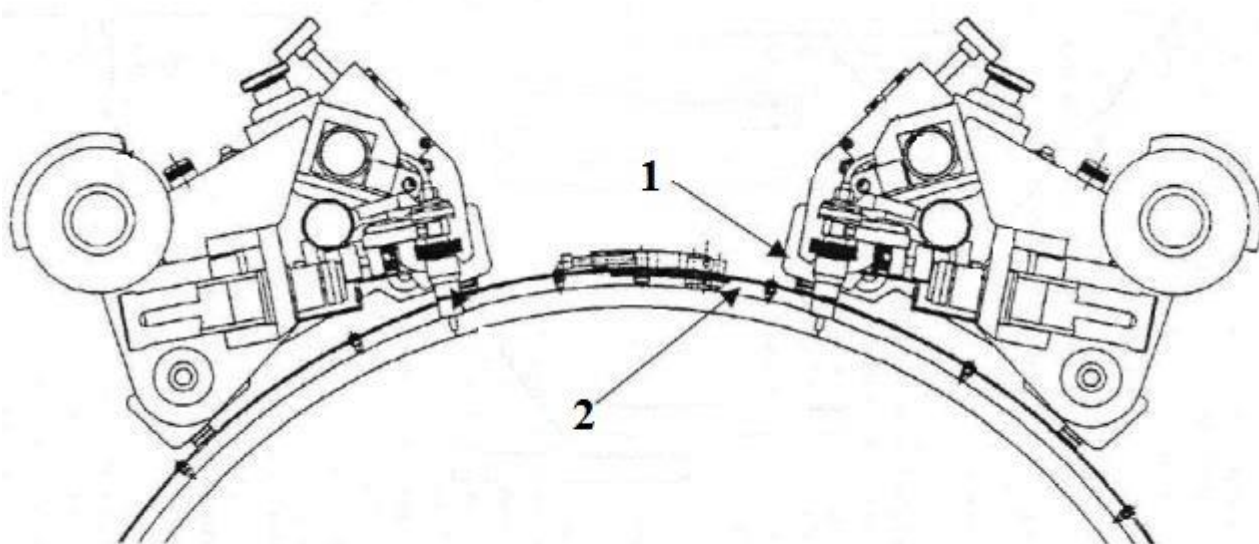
Наружные сварочные головки CRC-EVANS:
